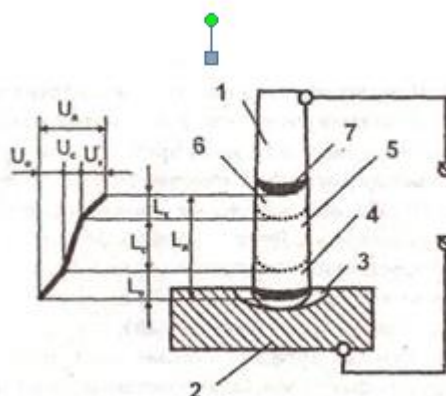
Схема сварочной дуги и падения напряжений в ней:
